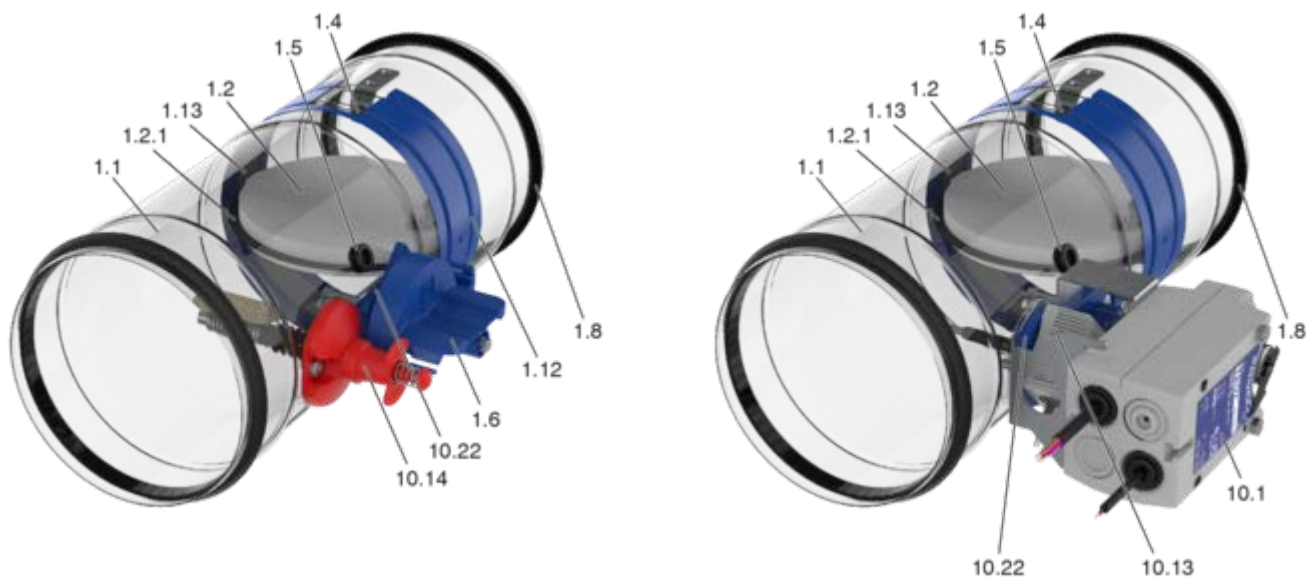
FKRS-EU med smältsäkring eller fjäderåtergångsmotor
